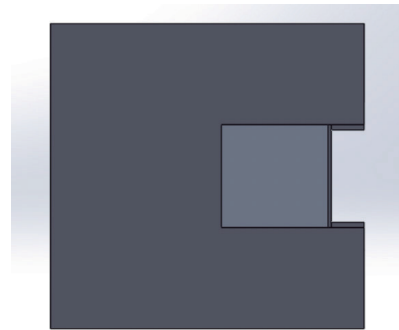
Caja donde estará el transformador en la máquina de soldadura por puntos, vista superior.
